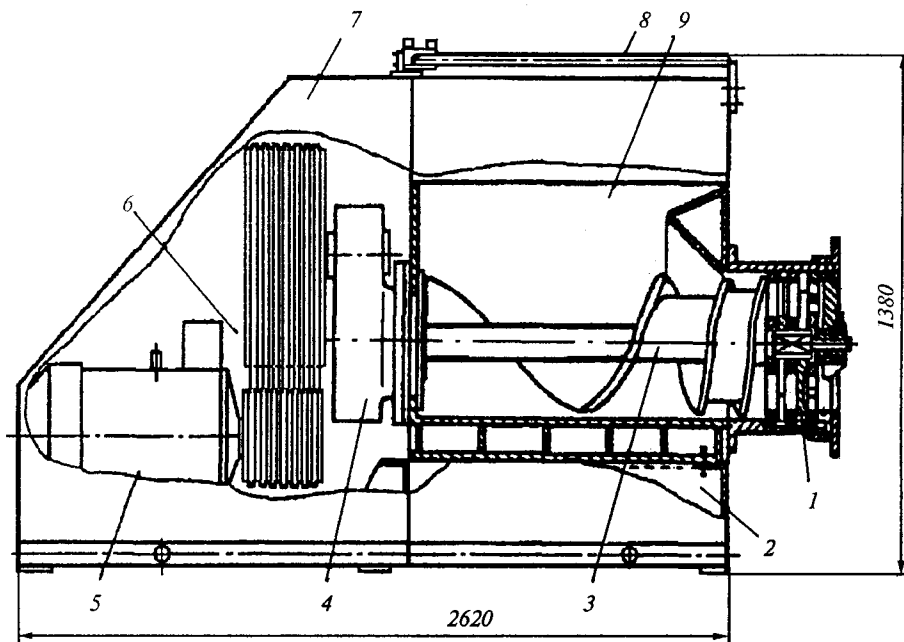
Волчок-дробилка В2-ФД2-Б
